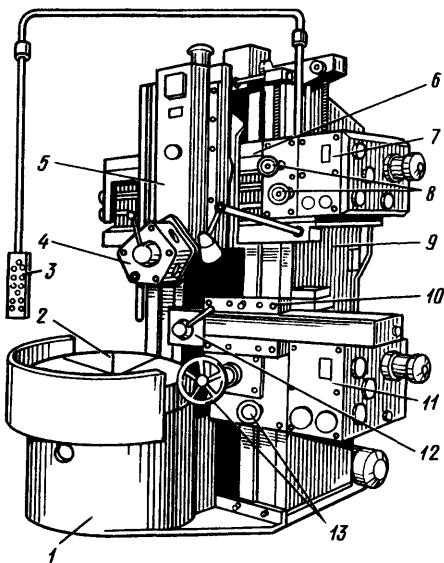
Одностоечный токарно-карусельный станок модели 1512
